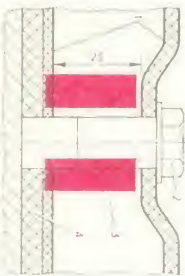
Установка распорных втулок: 1 — стенки корпуса воздухозаборника; 2 — гайка; 3 — дополнительная втулка; 4 — штатная прокладка.
